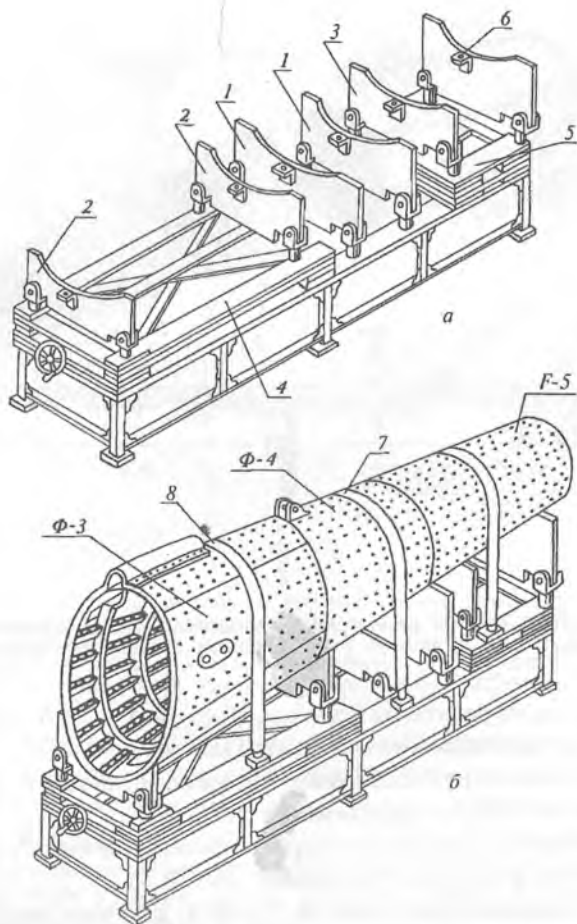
Стенд для сборки-стыковки отсеков в агрегат:
